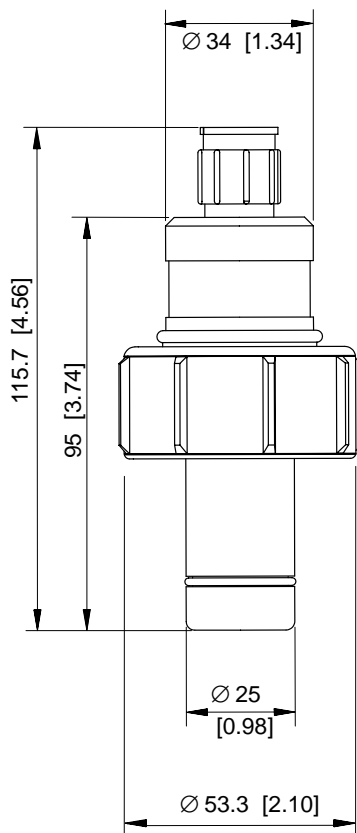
Esquema de dimensiones de InPro®7100-25/7104-25 de célula de 4 electrodos.
